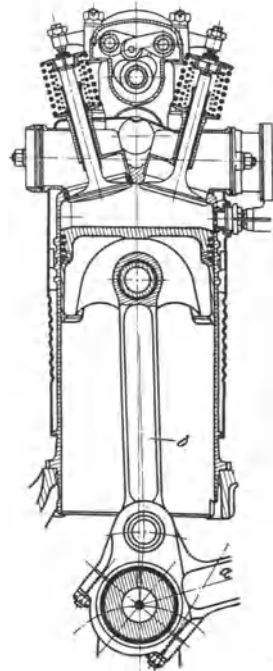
Wassergekühlter Flugmotor-Stahlzylinder mit angeschweißtem Mantel und Kopf. Bohrung 160 mm, Hub 190 mm. Hauptpleuelstange *a*, Nebenpleuelstange *b*.
